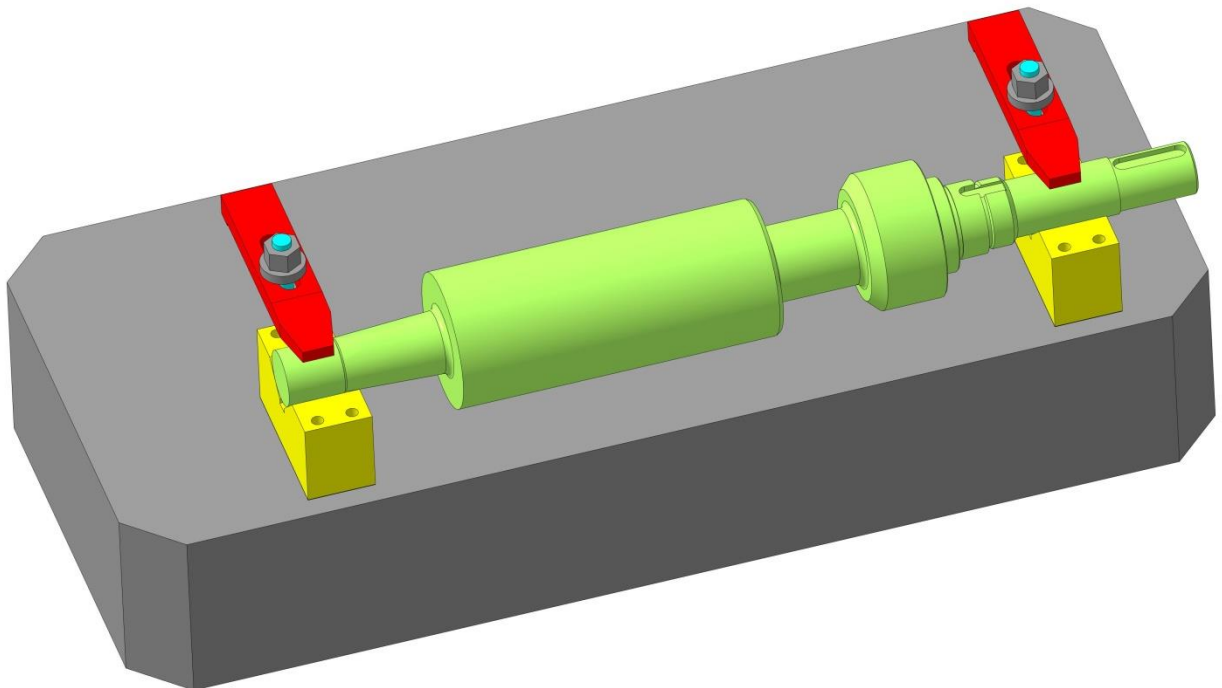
Спроектований верстатний пристрій для комплексної операції та закріплена деталь
